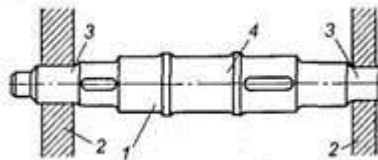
Прямой вал: 1 — вал; 2 — опоры вала; 3 — цапфы; 4 — шейка
